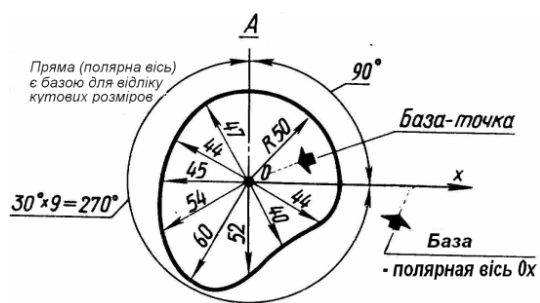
Розмірні бази – точка і лінії на прикладі типової деталі (кулачок)
